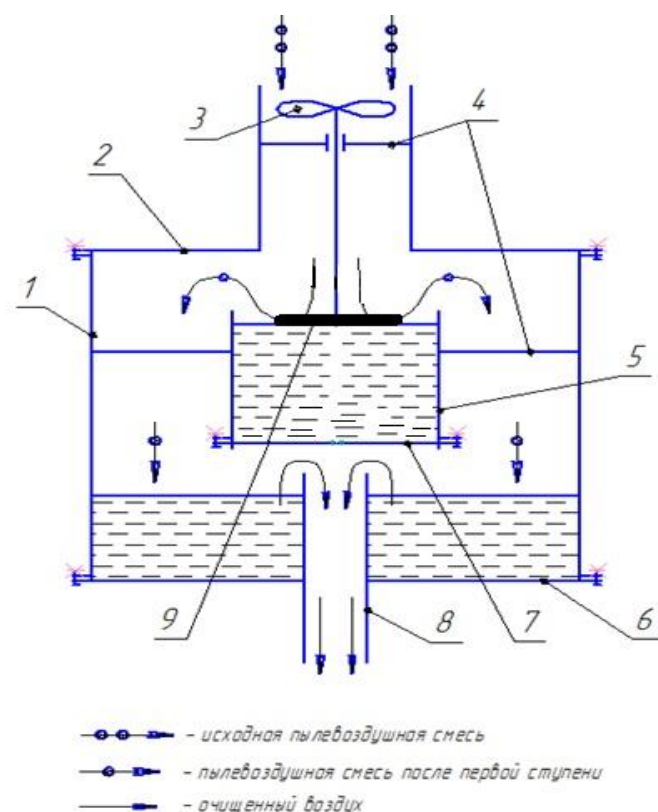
Схема мокрого пылеуловителя: 1 – корпус; 2 – крышка верхняя с патрубком; 3 – вентилятор с валом; 4 – спицы; 5 – корпус первой ступени; 6 – крышка; 7 – крышка первой ступени; 8 – отводящий патрубок; 9 – мешалка
